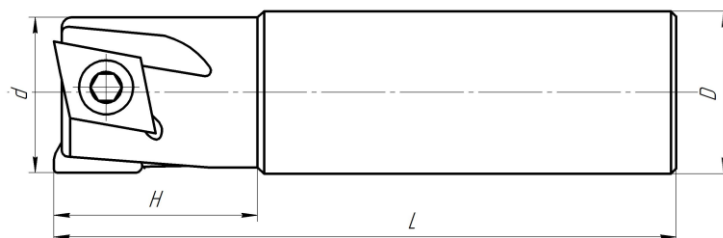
Кінцева фреза T290 ELN D20-05-C16-05
